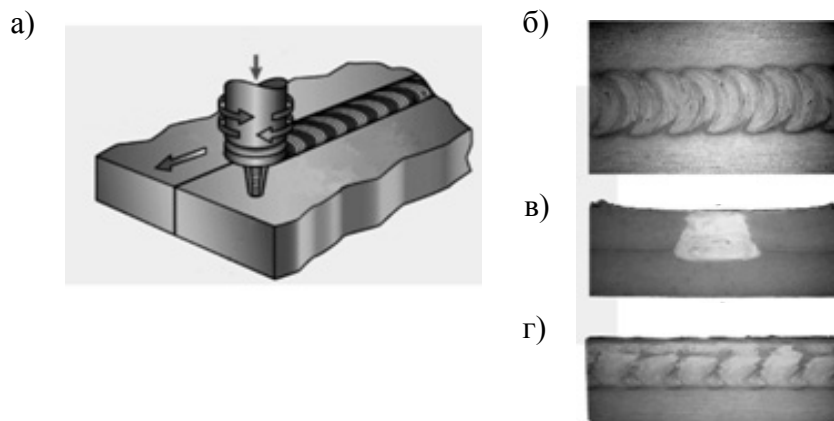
СТП с возвратно-вращательным движением инструмента: а – схема сварки; б – вид сварного шва; в – сечение, перпендикулярное направлению шва; г – сечение вдоль шва
